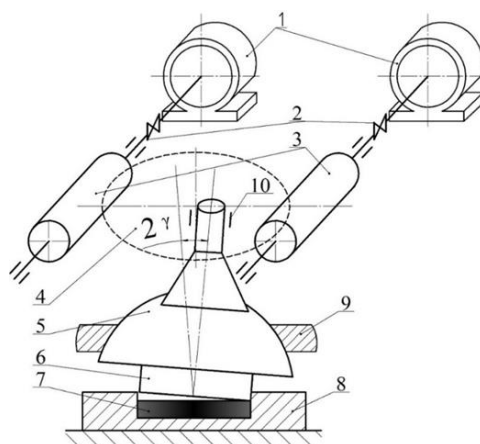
Кинематическая схема сферодвижного механизма Силичева:
